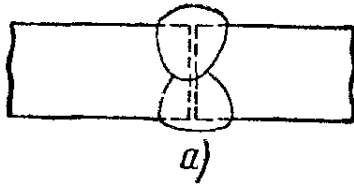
Подготовка кромок при сварке под флюсом:
